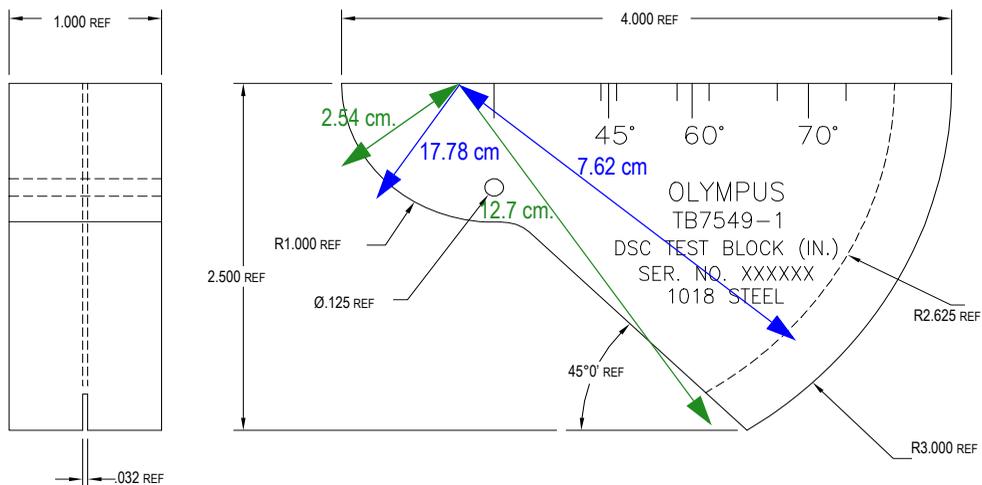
Калибровочный образец расстояния и чувствительности (Арт.: ТВ7549-1)
